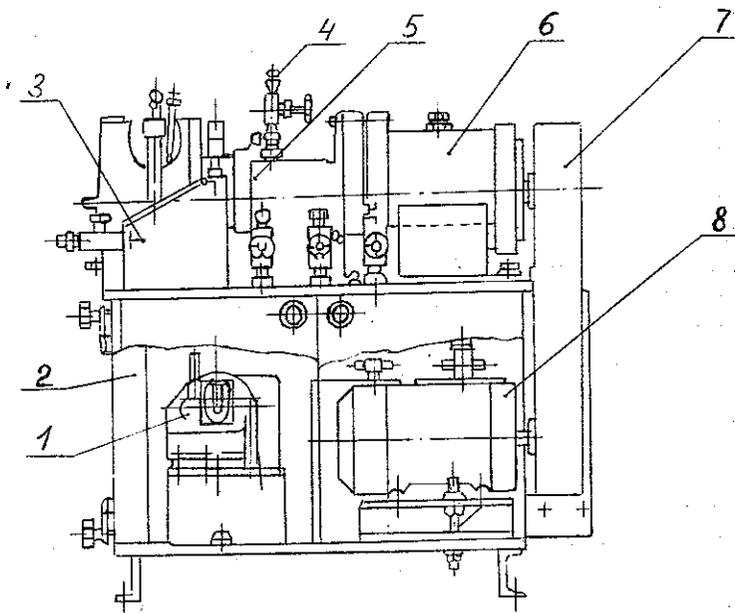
Стенд для испытания торцовых уплотнений:
